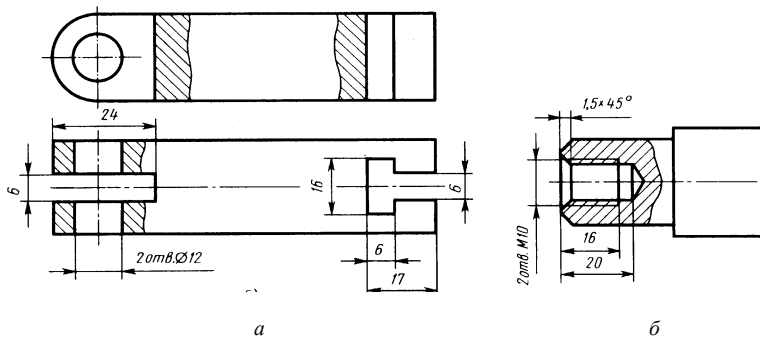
Группировка размеров: а – для паза; б – для отверстия
